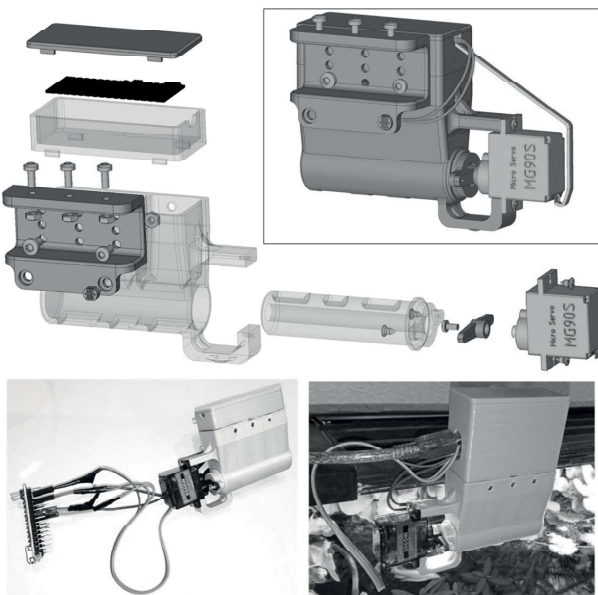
Автоматическая кормушка для рыб (модель T-Flex CAD 3D и реальное устройство)
